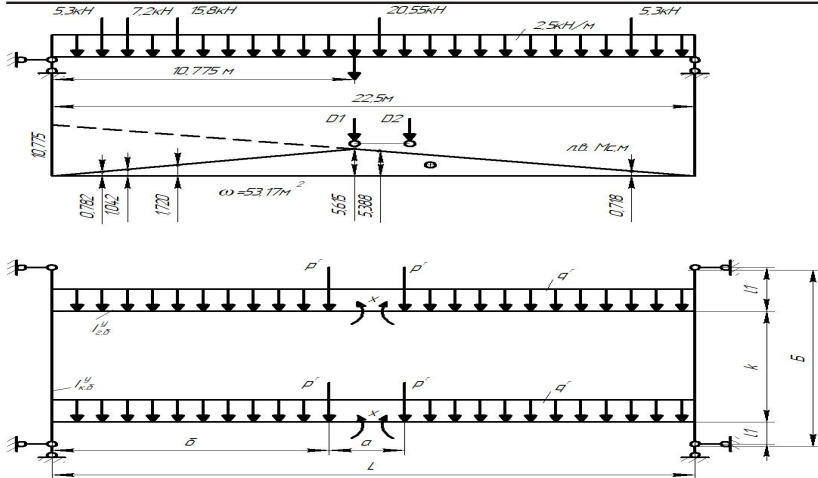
Расчетная схема моста крана при расчетах на вертикальные нагрузки. Определение изгибающих моментов в опасном сечении главной балки методом линий влияния
